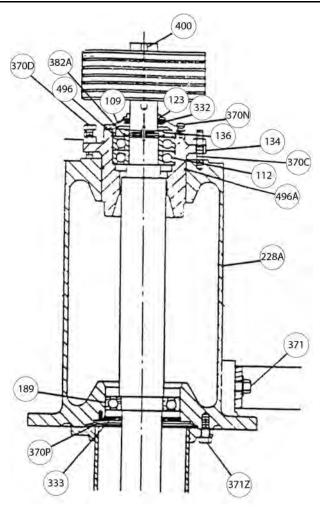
Desmontaje de la carcasa de rodamientos y el eje
